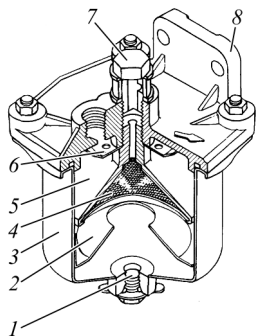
Фильтр грубой очистки топлива: 1 – пробка; 2 – успокоитель; 3 – стакан; 4 – сетка; 5 – отражатель; 6 – рассеиватель; 7 – болт поворотного угольника; 8 – корпус фильтра
